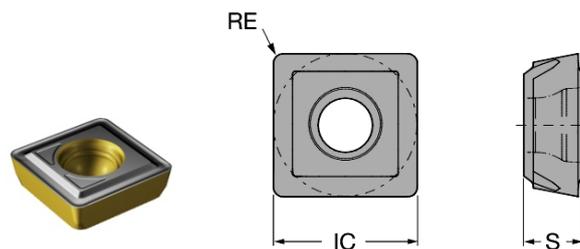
Режущая пластина для сверла CoroDrill® 880-04 03 W07H-P-GR 4324
